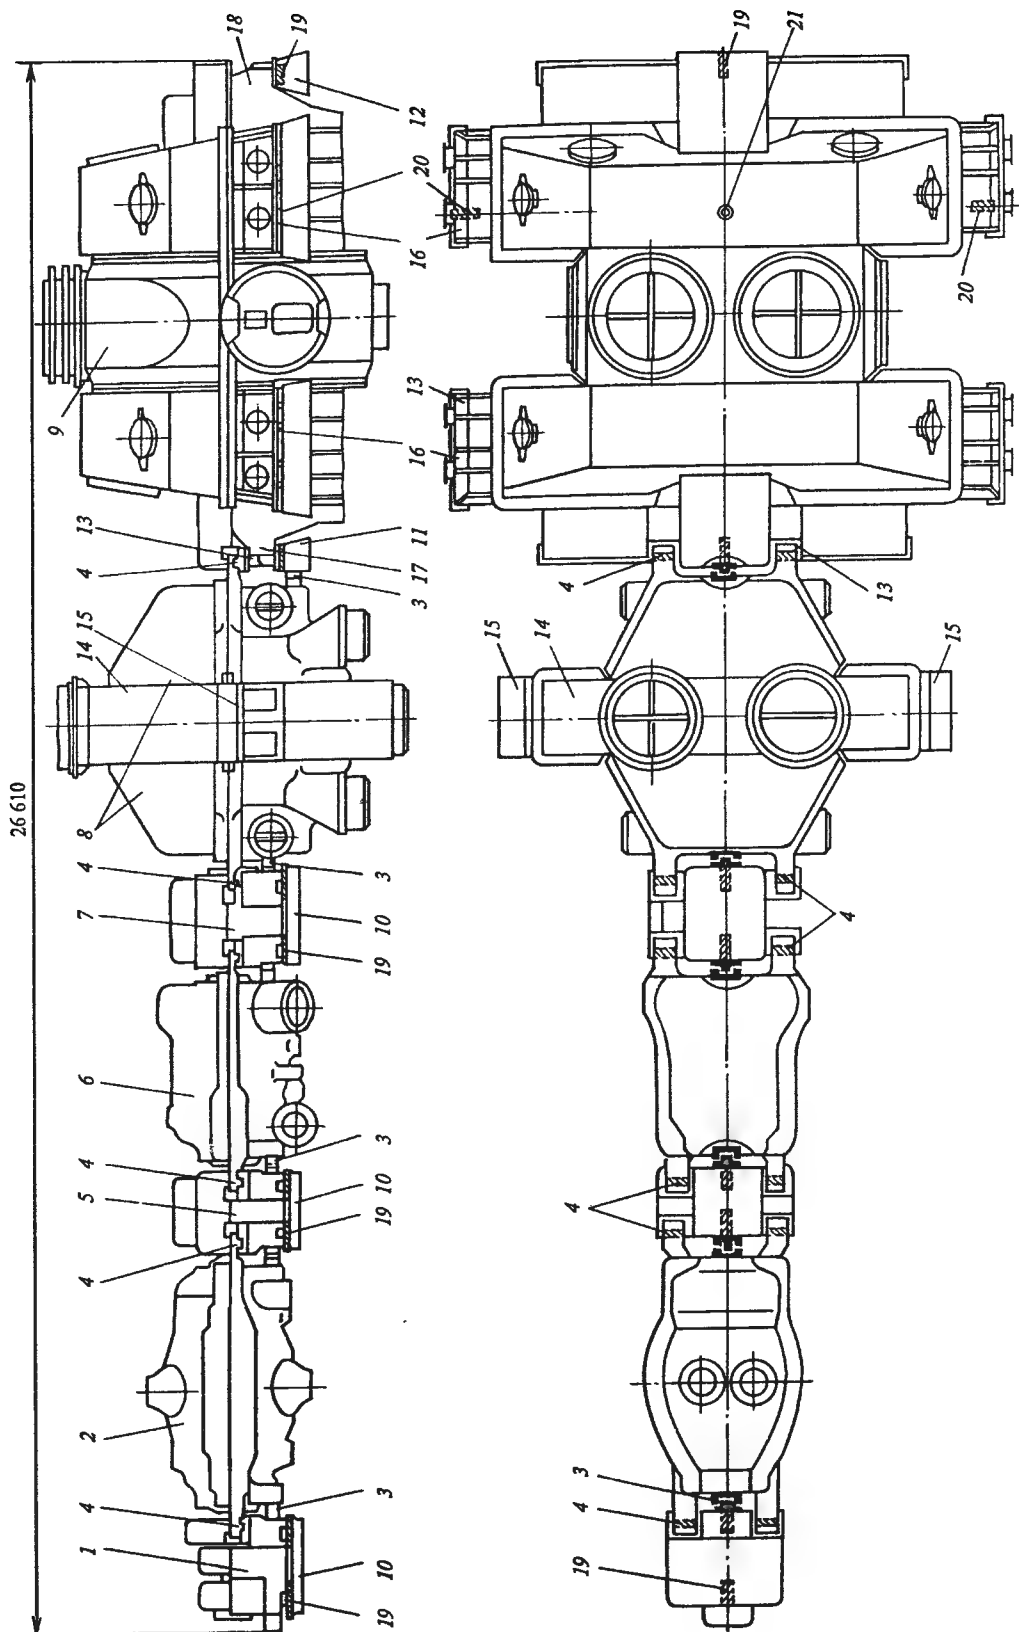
Опиране на фундамент турбини Т-250/300-23,5 ТМЗ:
